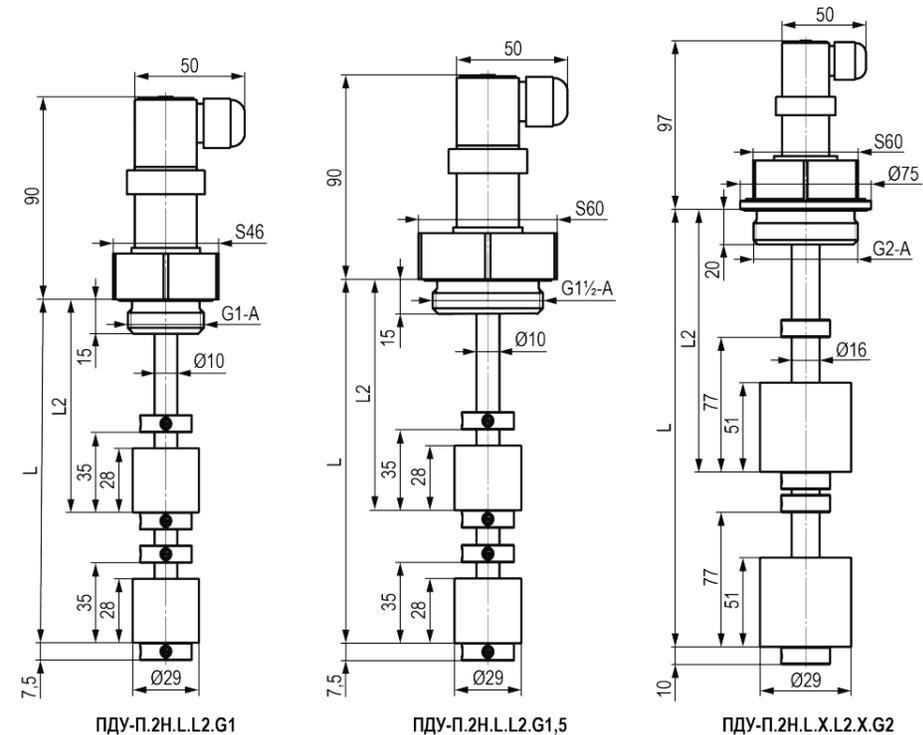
Габаритные и присоединительные размеры двухуровневых ПДУ-П с разъемом DIN 43650 А (наружный монтаж)
